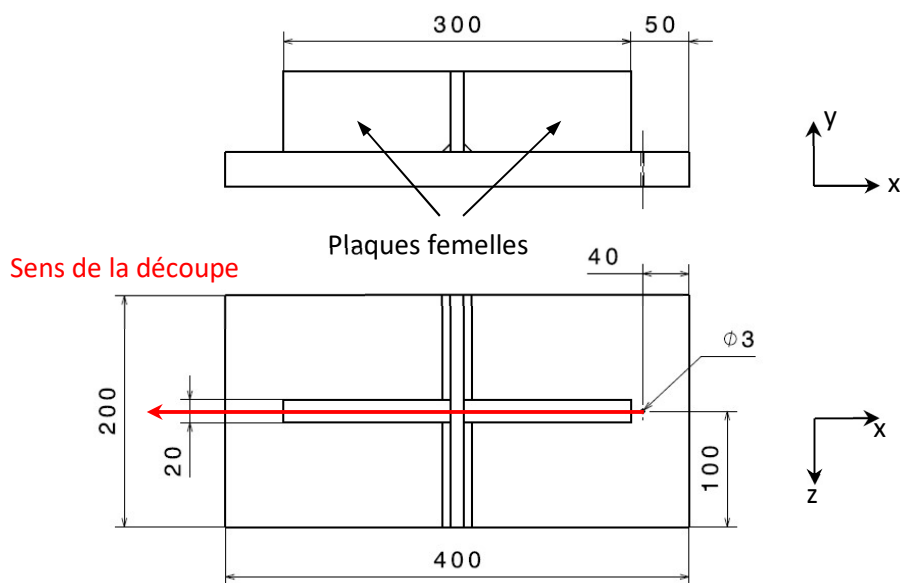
Ajout des plaques femelles pour la découpe par électroérosion - dimensions en (mm)
